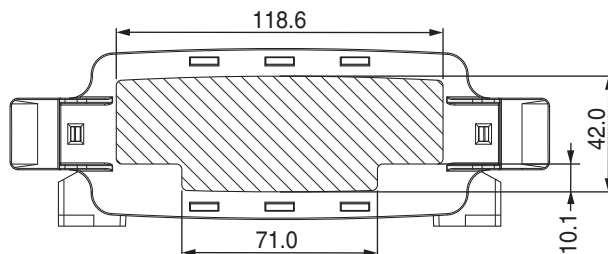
Verfügbare Montagefläche für Steckverbinder bei ECS-P...B
